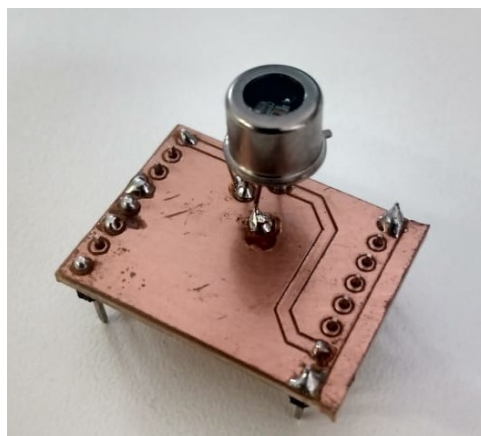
PCB implementada com o sensor *GUVCL-T21GH
